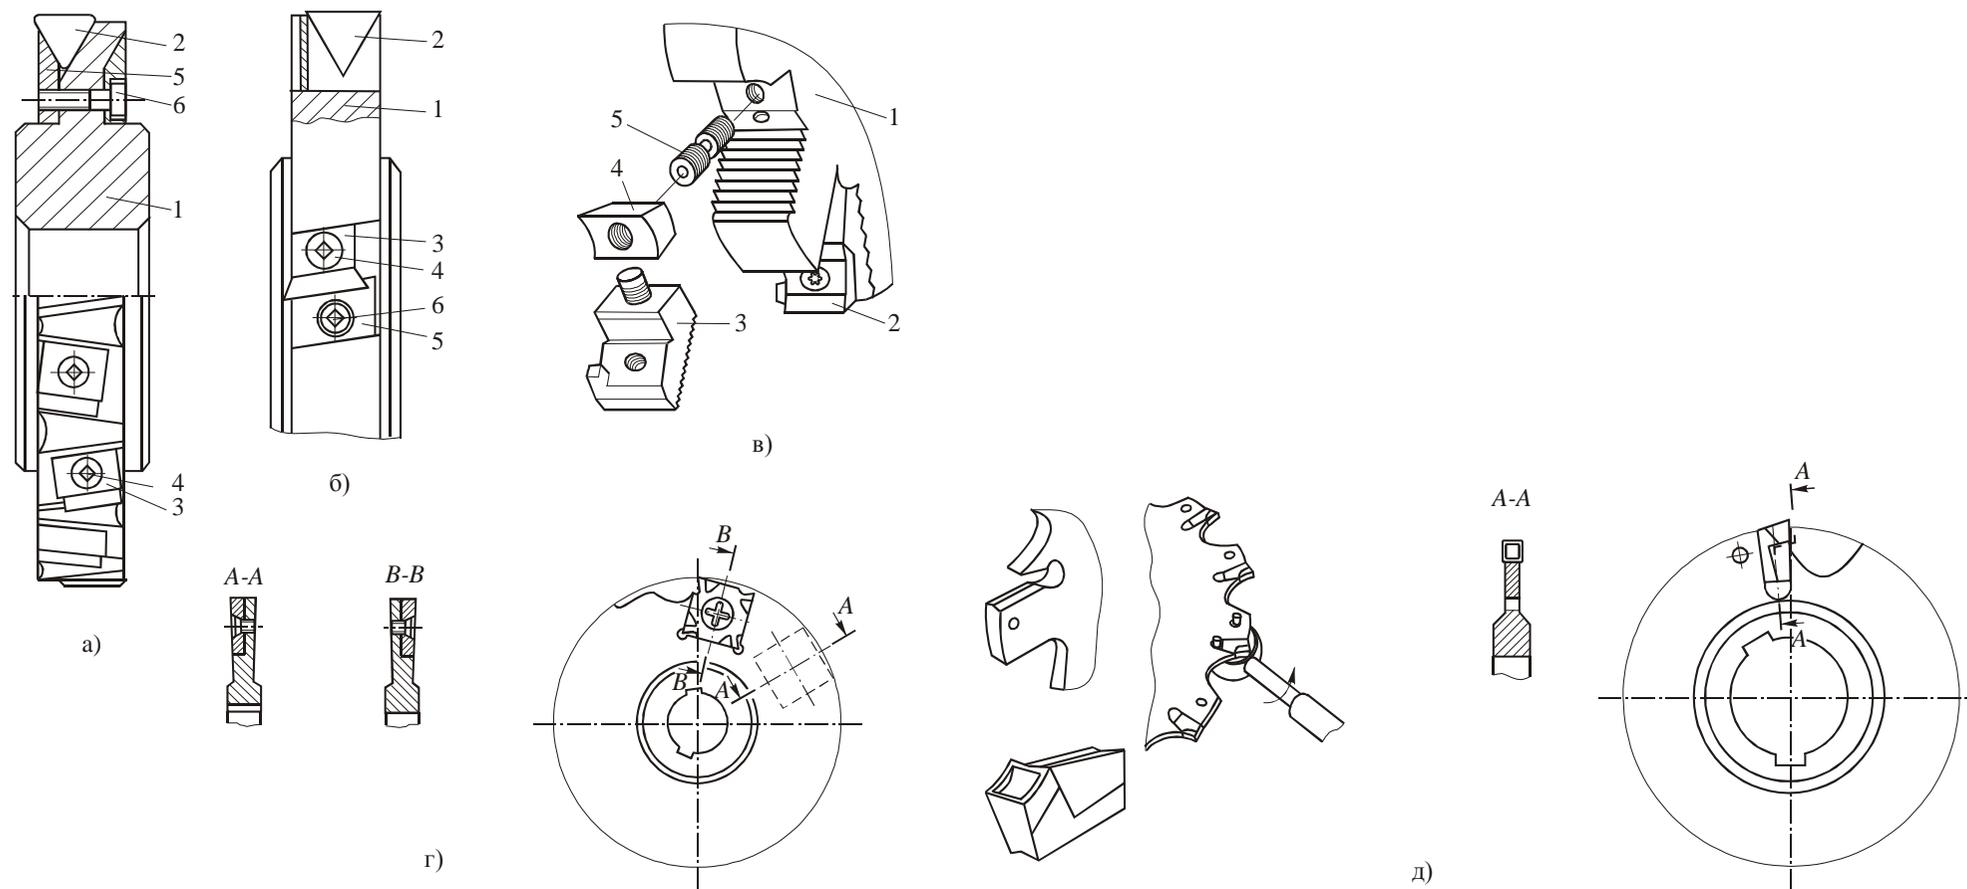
Дисковые фрезы, оснащенные СМП: *а* – трехсторонняя с «открытыми» базами под пластины; *б* – трехсторонняя с базированием пластин во вкладышах; *в* – с креплением пластин и вкладышей винтами; *г* – с тангенциальным креплением пластин; *д* – со специальными пластинами для отрезных работ (слева показана схема снятия пластины)
